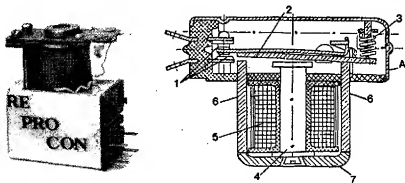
Реле «Репрокон» с отдельной герметичной оболочкой для контактов, разработанное автором: 1 — контакты; 2 — якорь клапанного типа; 3 — возвратная пружина; 4 — ферромагнитный сердечник; 5 — обмотка; 6 — пластины магнитопровода, запрессованные в герметичную оболочку А; 7 — замыкающая пластина магнитопровода, монтируемая после установки обмотки
